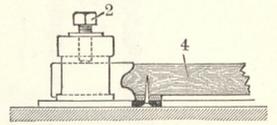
Fräser einer Holzfräsmaschine (Fräsen eines Profils nach Schablone).
